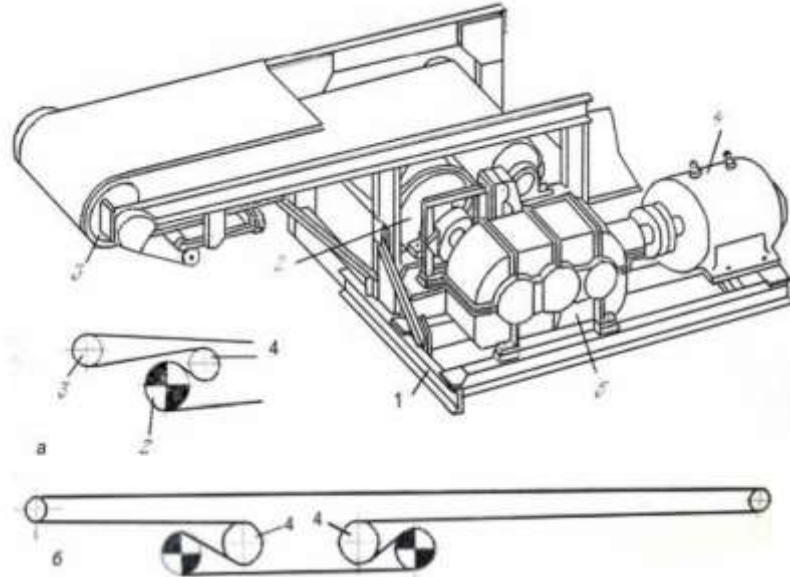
Конструкція та схеми приводу стрічкових конвеєрів: а) – з одним приводним барабаном; б) – з двома приводними барабанами. 1 - рама, 2 - приводний барабан, 3 - розвантажувальний барабан, 4 - електродвигун, 5 - редуктор, 4 – відхиляючий барабан, 6 – електродвигун, 7 – натяжний барабан.
